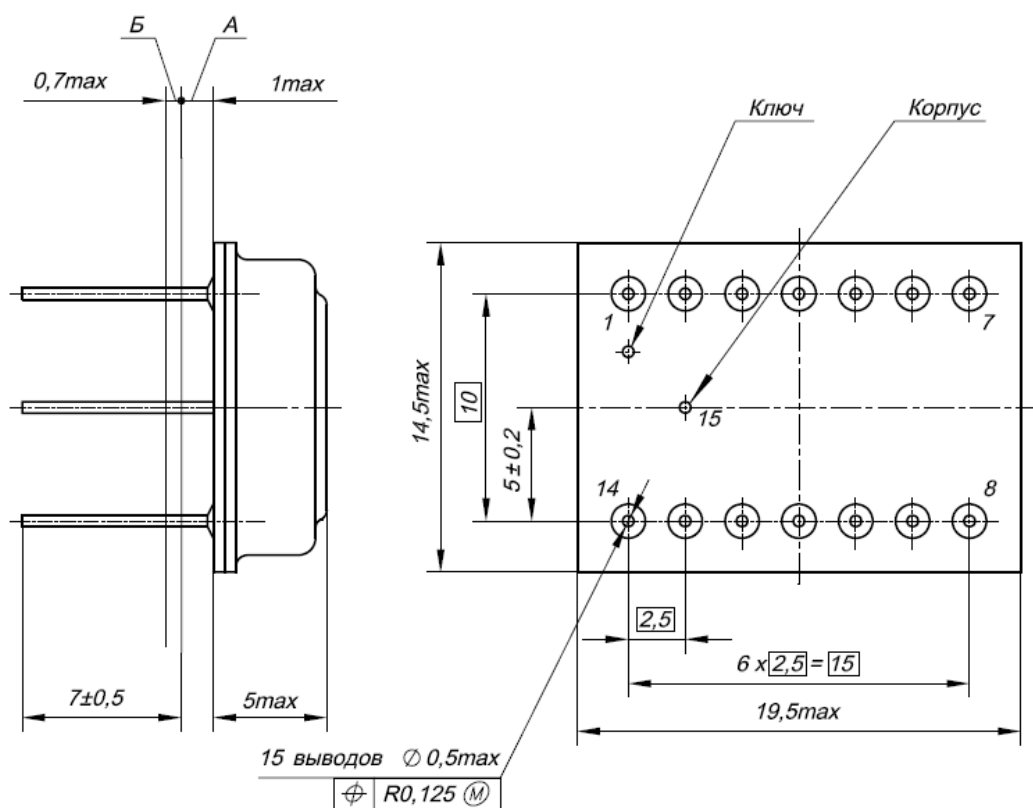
Габаритный чертеж корпуса 151.15-8
